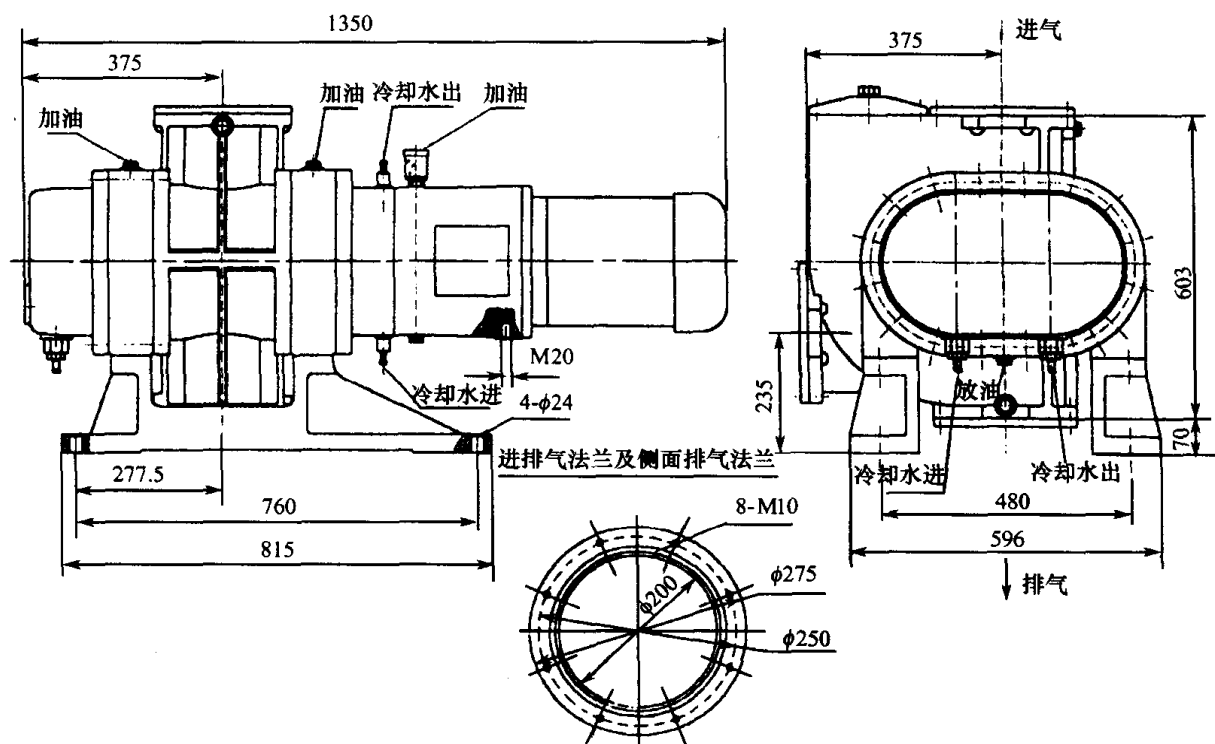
ZJP-600 型罗茨泵外形及安装尺寸
